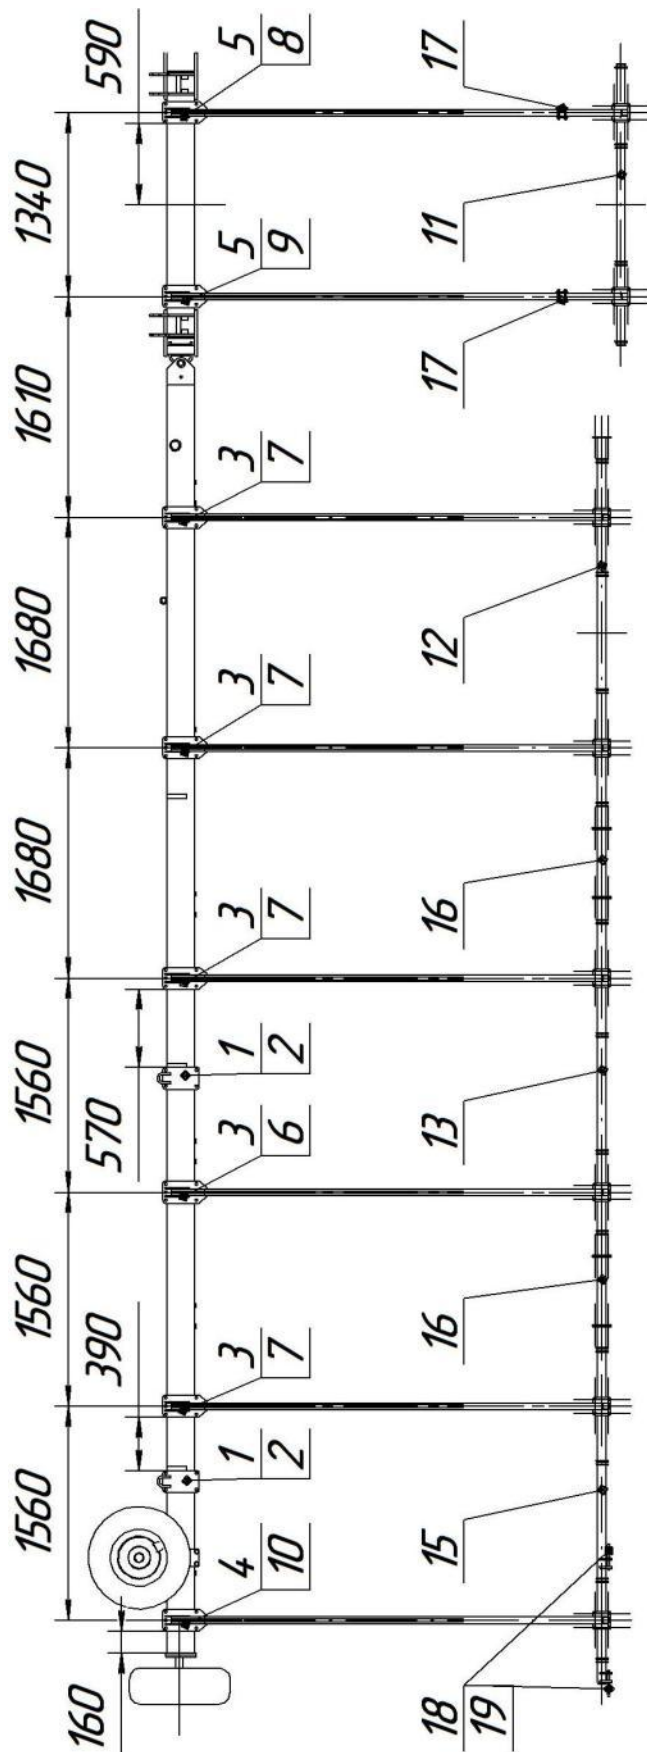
б. Продольные балки, поперечины и петли для троса БГУ-20-Ш
